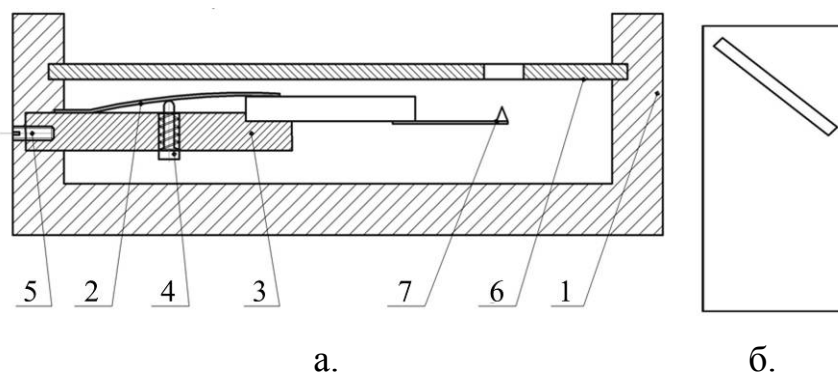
Схематичне зображення тримача для зондів: а – переріз профілю тримача; б – вигляд на тримач згори; 1 – корпус тримача; 2 – жорстка пластина; 3 – столик; 4 – кнопка відхилення жорсткої пластини; 5 – шпилька; 6 – маска, вид згори (б); 7 – чутливий елемент АСМ
